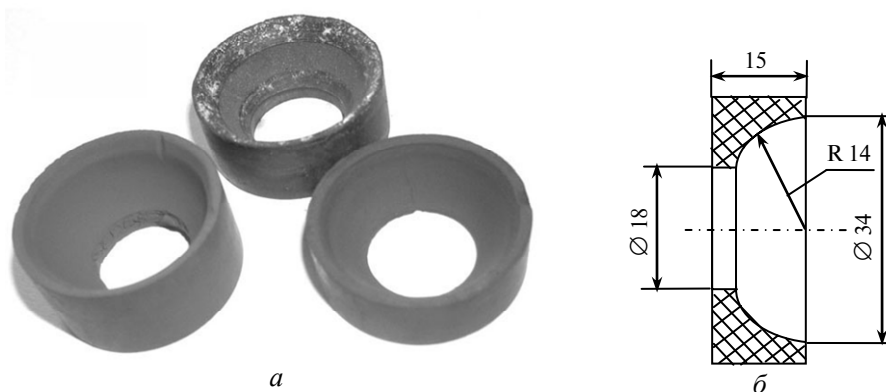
Притиры для алмазно-абразивной обработки титановой заготовки: фотоснимок (а) и чертеж (б) инструментов.
